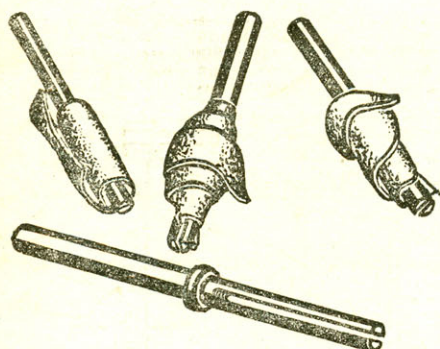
Шлифовальные головки из шкурки и оправка к ним.
